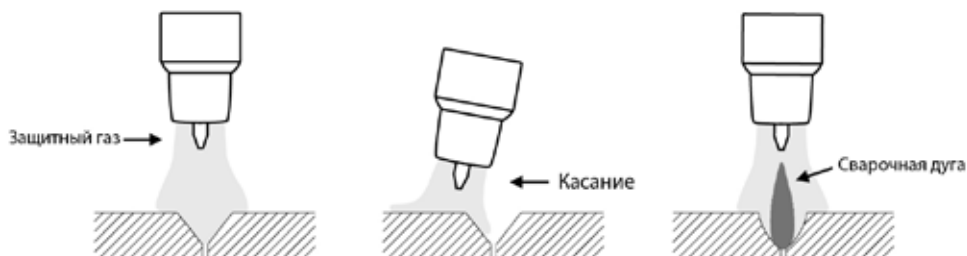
Процесс образования сварочной дуги.
